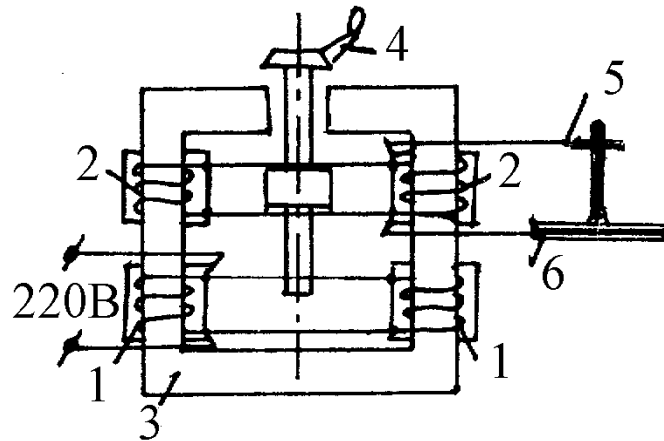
Принцип работы сварочного трансформатора
